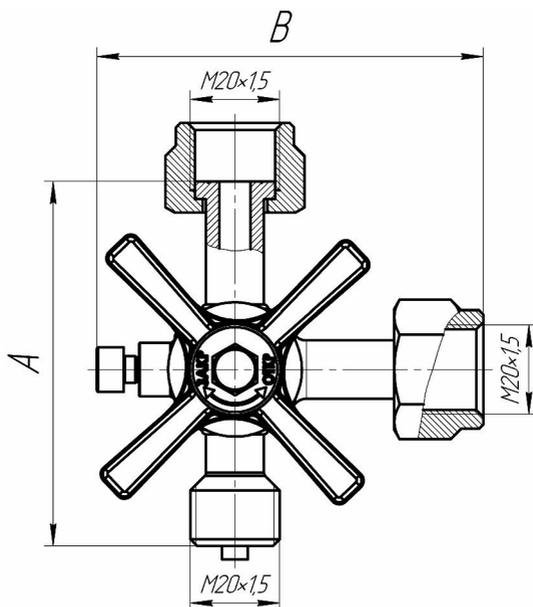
Габаритные и присоединительные размеры изделий
